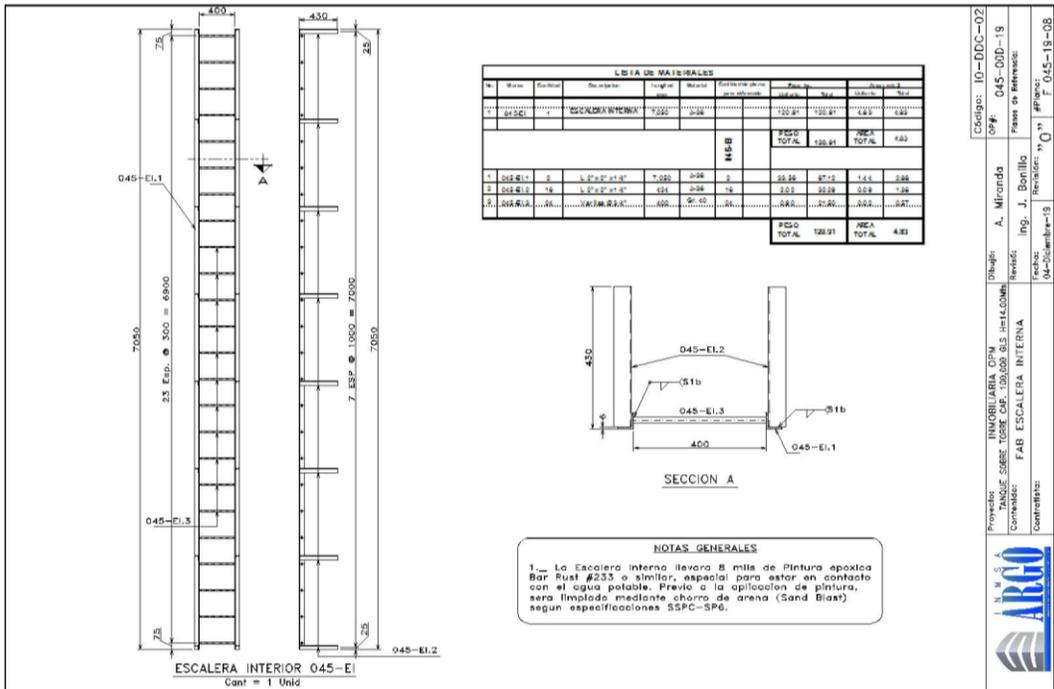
Plano para la fabricación de escalera interna en tanque elevado
